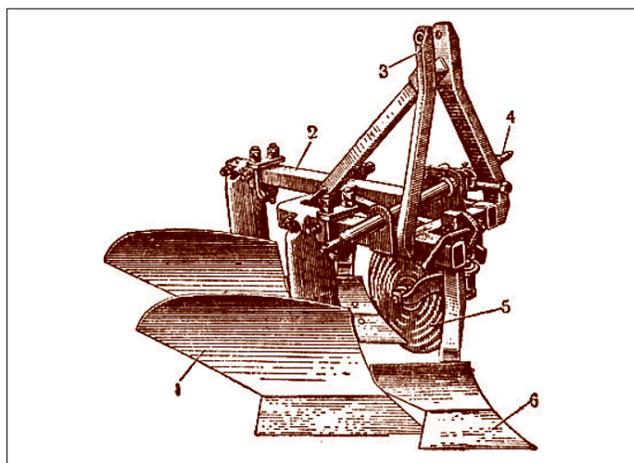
Навесной двухкорпусный плуг ПН-2-30-М: 1 – корпус; 2 – рама; 3 – кронштейн (стойка) навесного устройства плуга; 4 – ось подвески плуга; 5 – дисковый нож; 6 – предплужник
